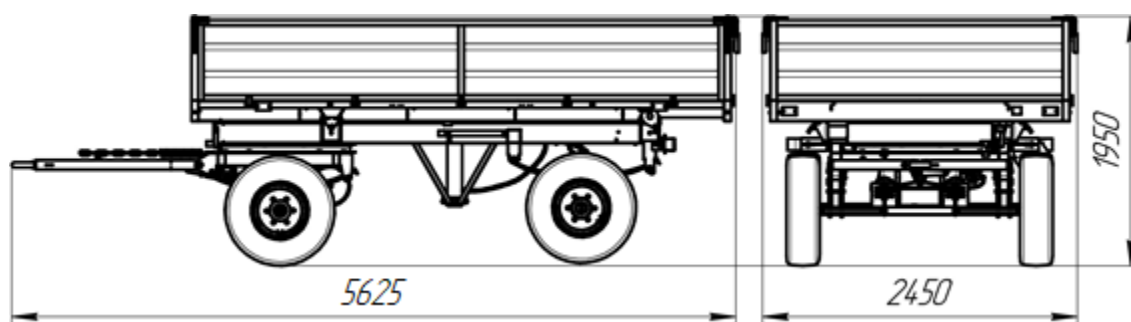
Габаритные размеры прицепа 2ПТС 6,5
